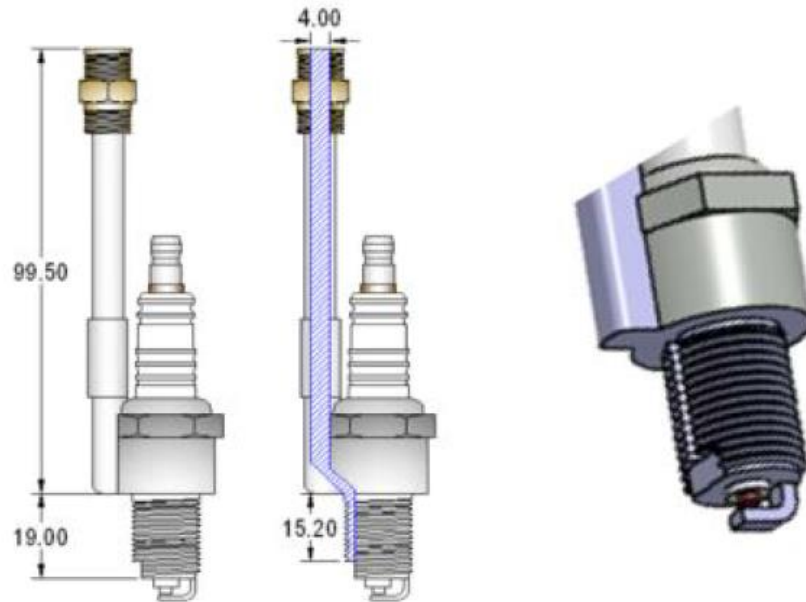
Свічка запалювання та детальний вигляд форсунки інжектора.
